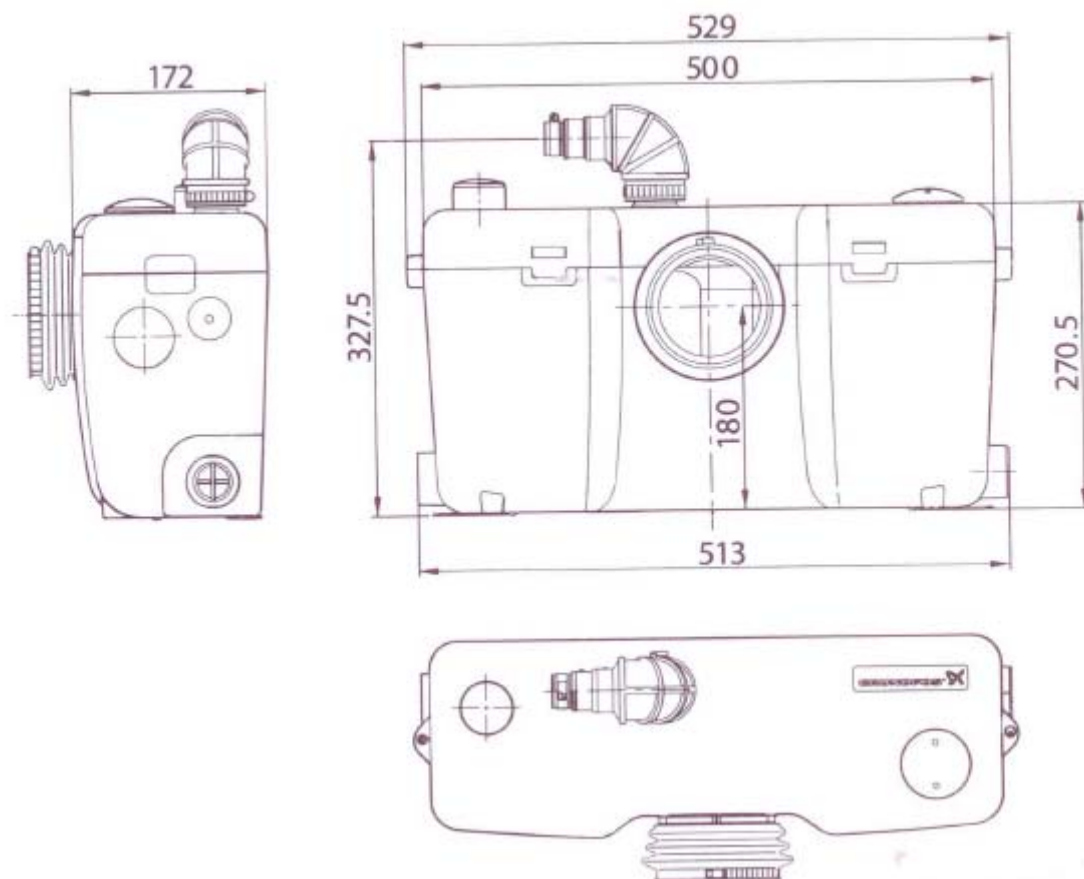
Габаритные размеры насосной установки SOLOLIFT2+ WC-3
